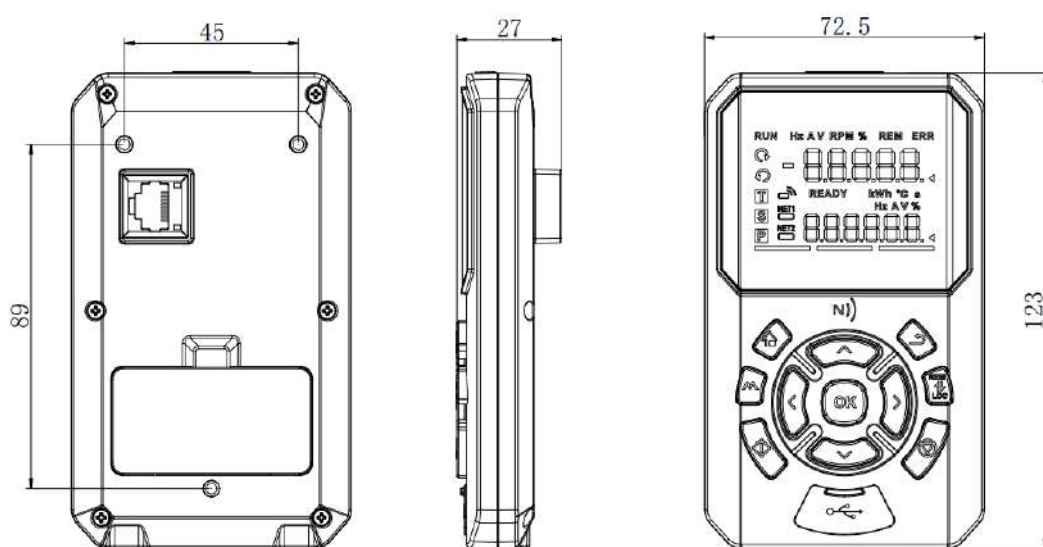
Внешний вид и монтажные размеры VT820-DP02 (в мм)
